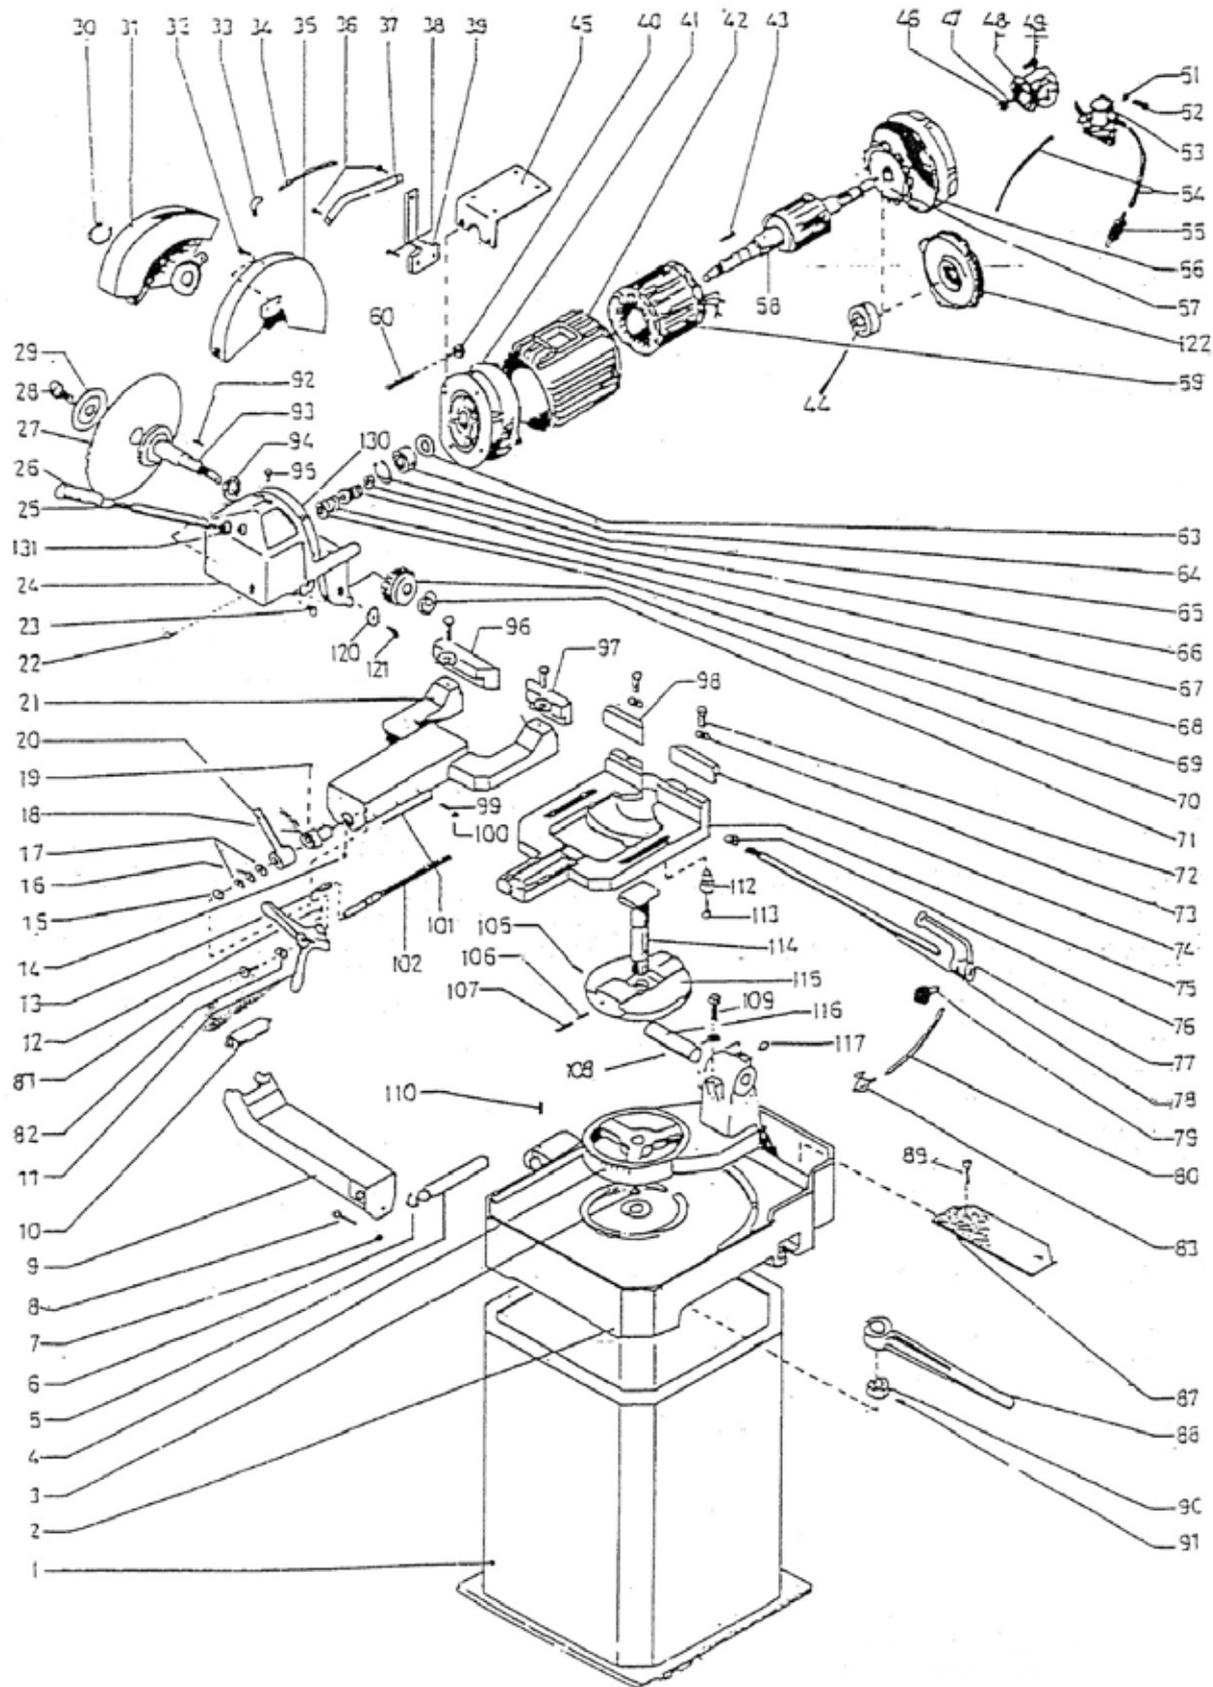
Dessin des pièces détachées 1 - MKS 315 N
